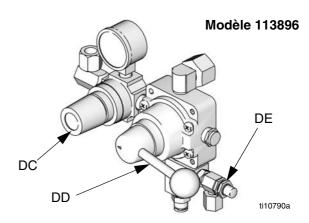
Ensemble de commandes pneumatiques d'élévateur
